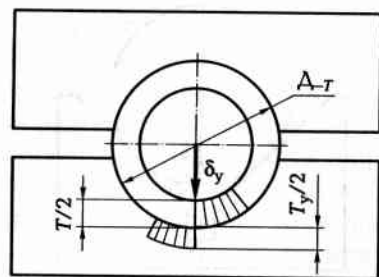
Схема установки цилиндрического вала в полуцилиндрическое отверстие установочного элемента приспособления
